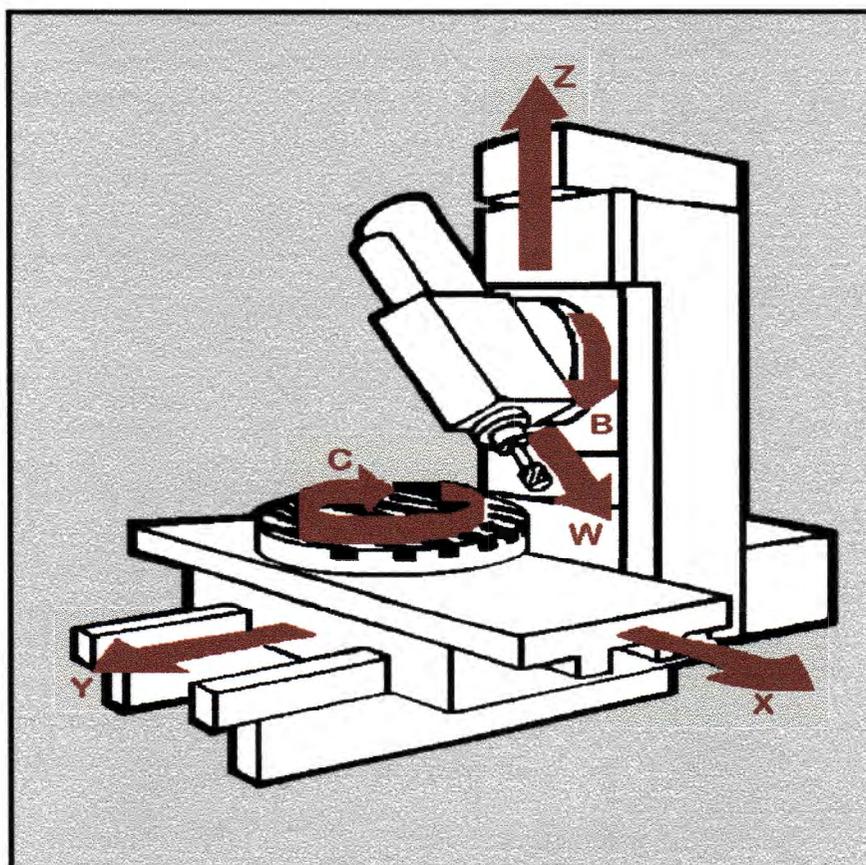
Centro de Usinagem com 6 Eixos (TRAUB, 1984)
